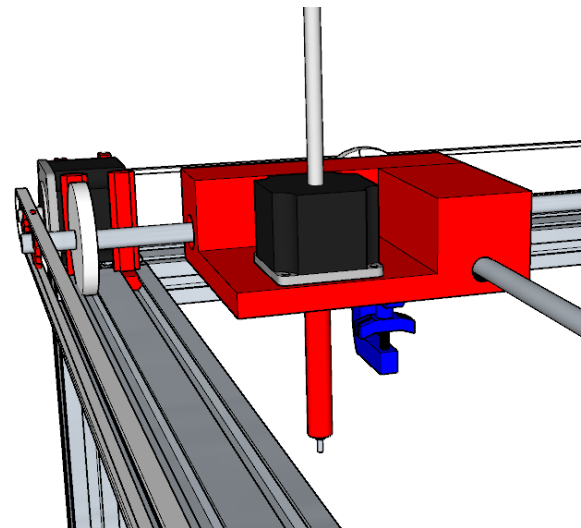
Detalhe do carro da área de irrigação e semeadura
